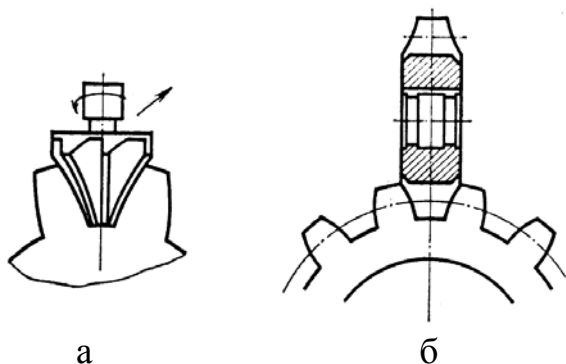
Фрезерування западин зуба методом копіювання: а – пальцевою фрезою; б – дисковою фрезою.
